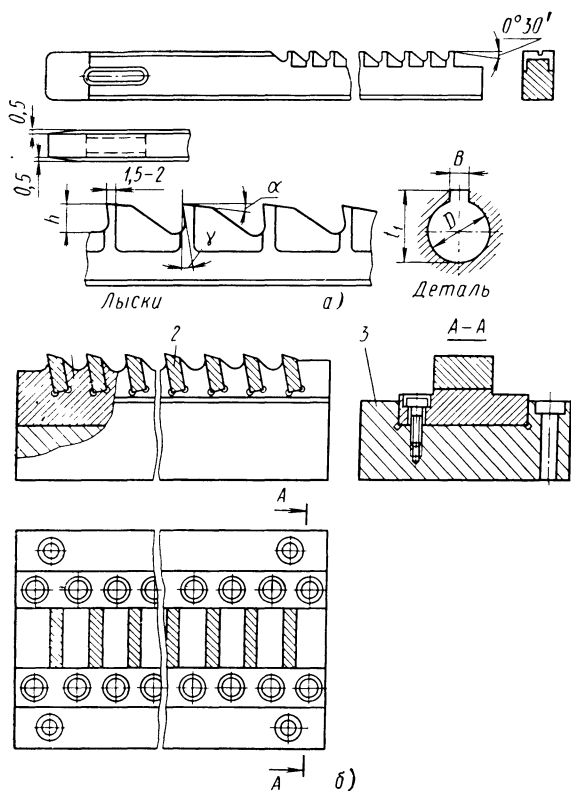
Протяжки, изготовленные из инструментальной стали и твердых сплавов:
